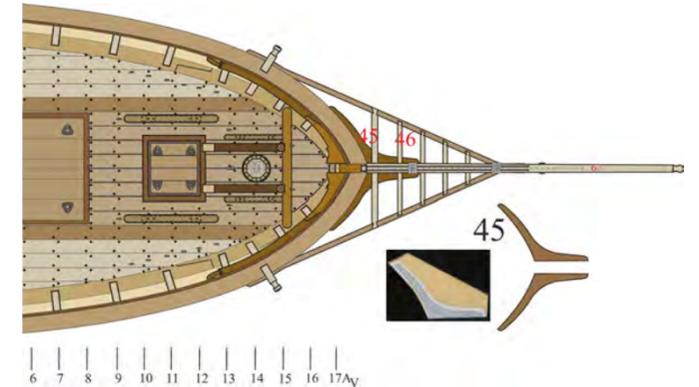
Vue de l'avant d'après la planche 13 et détail des courbâtons (45). Pour leur fabrication, faire référence aux cotes qui sont celles de la planche 15.
